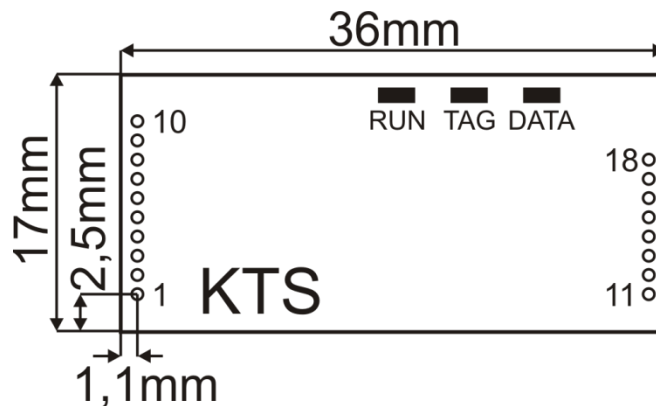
mechanical sketch - NOT technical drawing (for precise dimension please contact)
